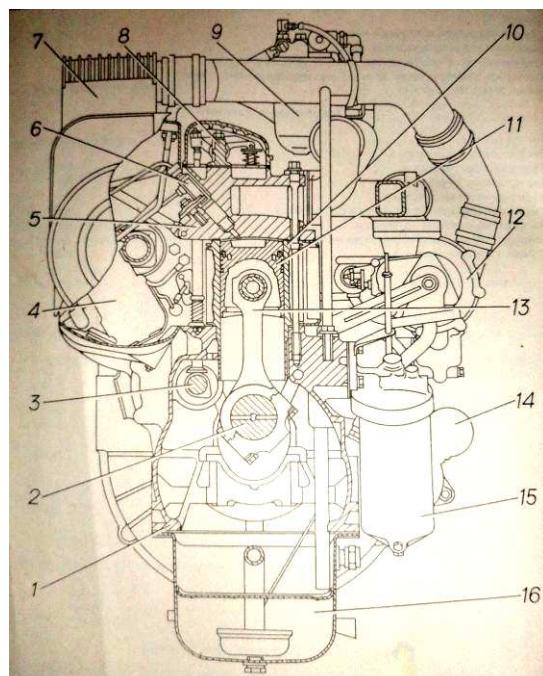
Поперечний розріз двигуна: 1 – картер двигуна; 2 – колінчастий вал; 3 – розподільний вал; 4 – паливний насос високого тиску; 5 – голівка циліндра; 6 – форсунка; 7 – охолоджувач наддувного повітря; 8 – привод клапанів; 9 – паливний фільтр; 10 – циліндр; 11 – поршень; 12 – турбокомпресор; 13 – шатун; 14 – стартер; 15 – масстильний фільтр; 16 – масстильний картер
